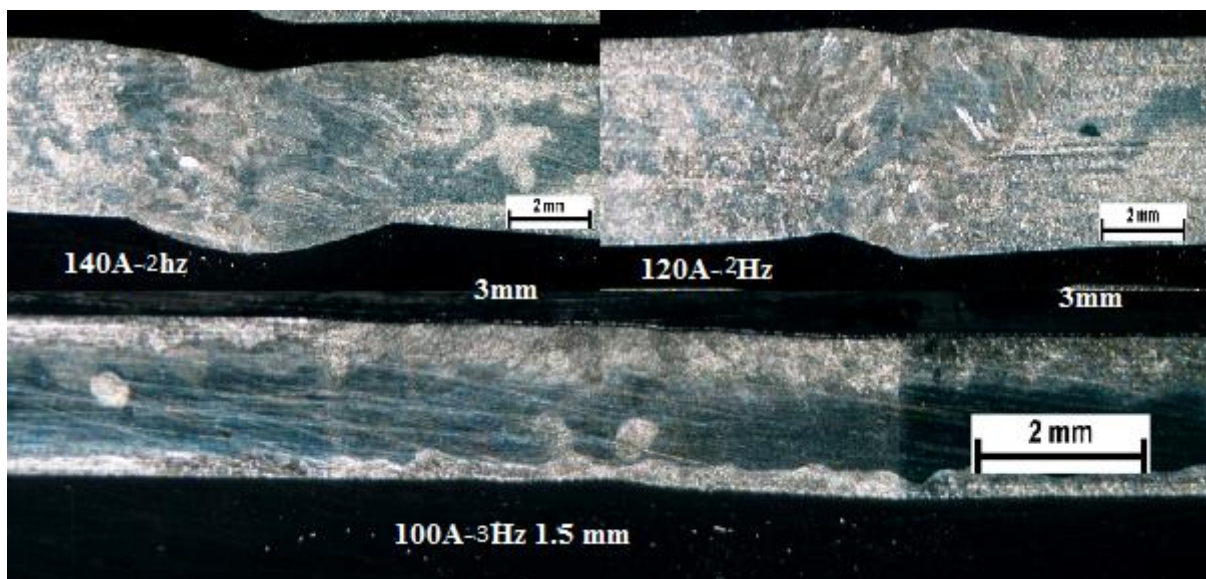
Macroscopie des soudures: Acier inoxydable, épaisseur 3 mm et 1.5 mm.
